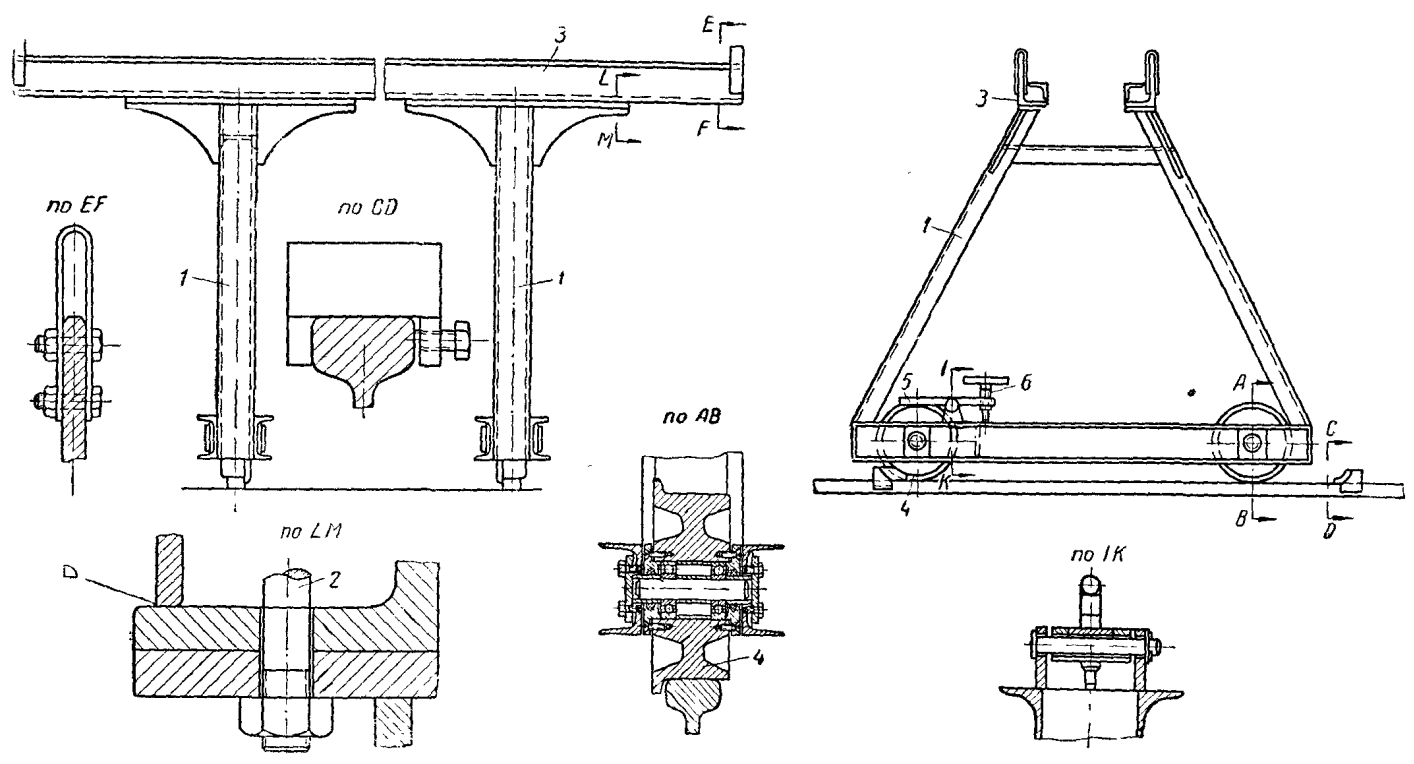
Приспособление для автоматической сварки продольных швов на трубах небольших диаметров.
